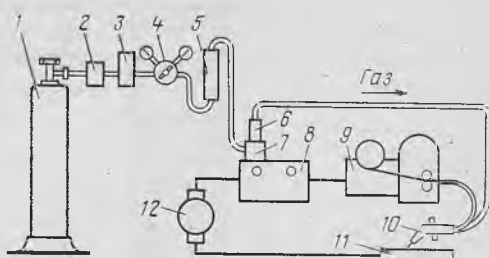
Схема установки для сварки (наплавки) в среде CO_2 :
